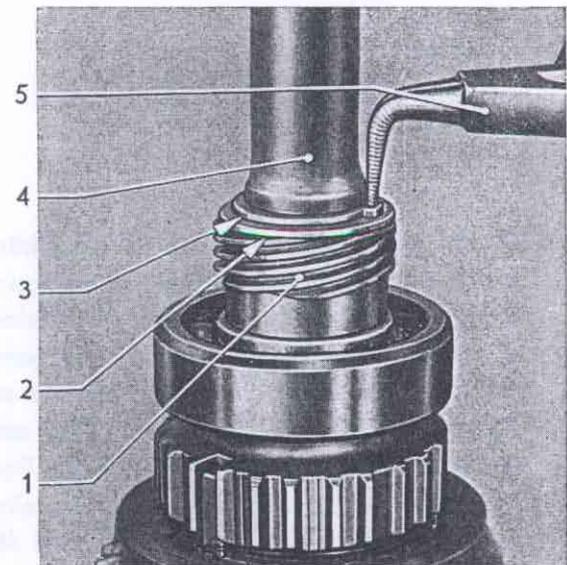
Tachometerschraubenrad durch Federscheibe und Sprengring auf Hauptwelle sichern
